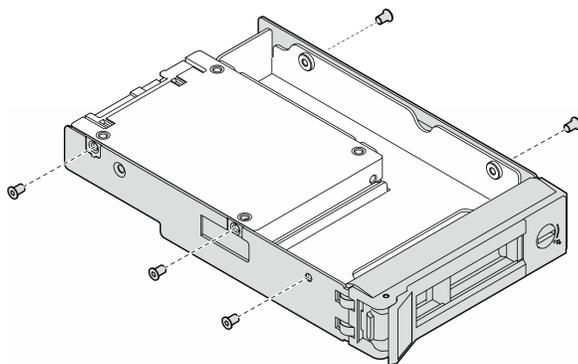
Installation der Schrauben, mit denen ein 2,5-Zoll-Laufwerk und ein Laufwerkadapter befestigt sind
